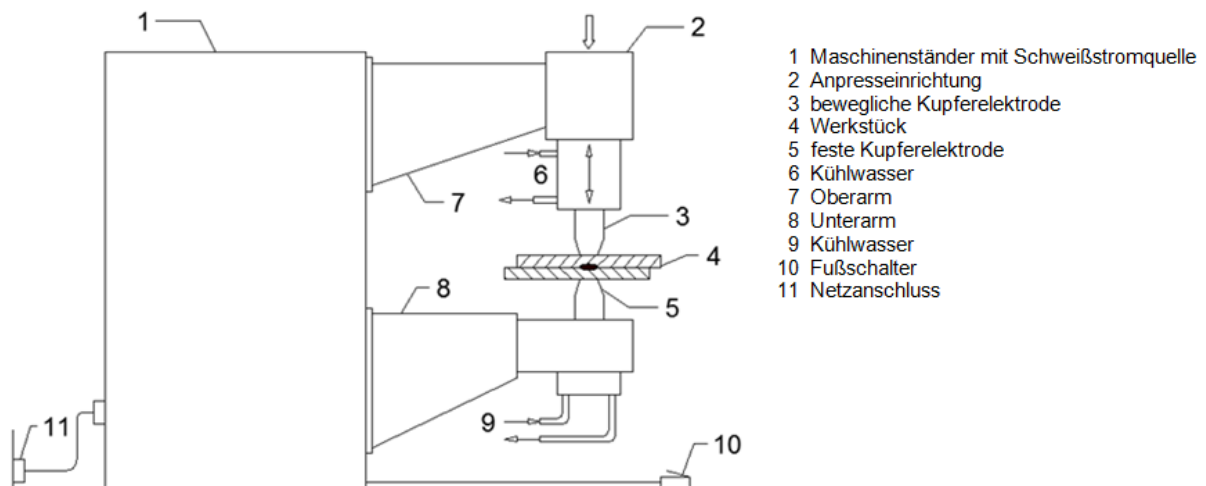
Widerstandspunktschweißen^[16]
